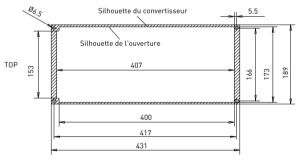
dimensions de découpe en montage par bride, pour MI5 (unité: mm)
